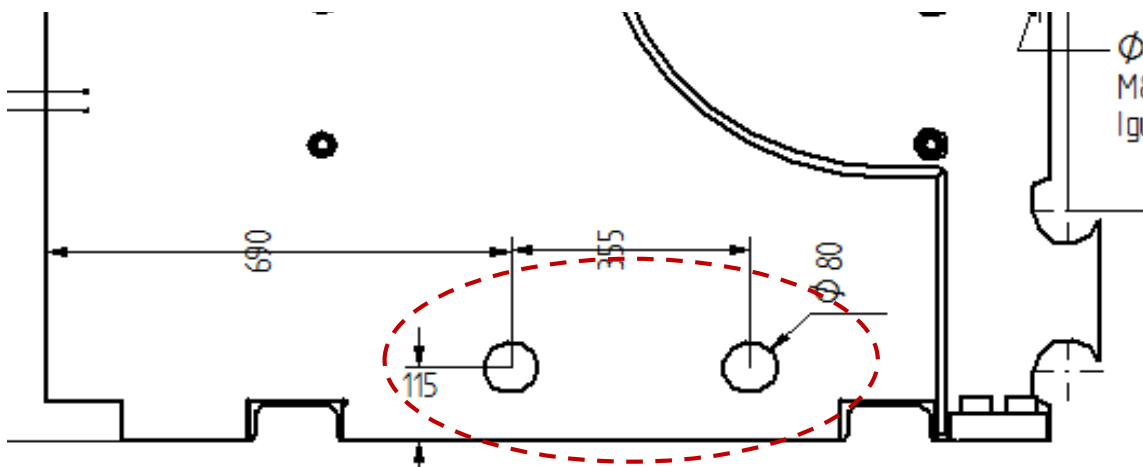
Desenho parcial da vista lateral do montante da máquina BB5020 com destaque para a interface de passagem de cabos e de fixação da máquina.
